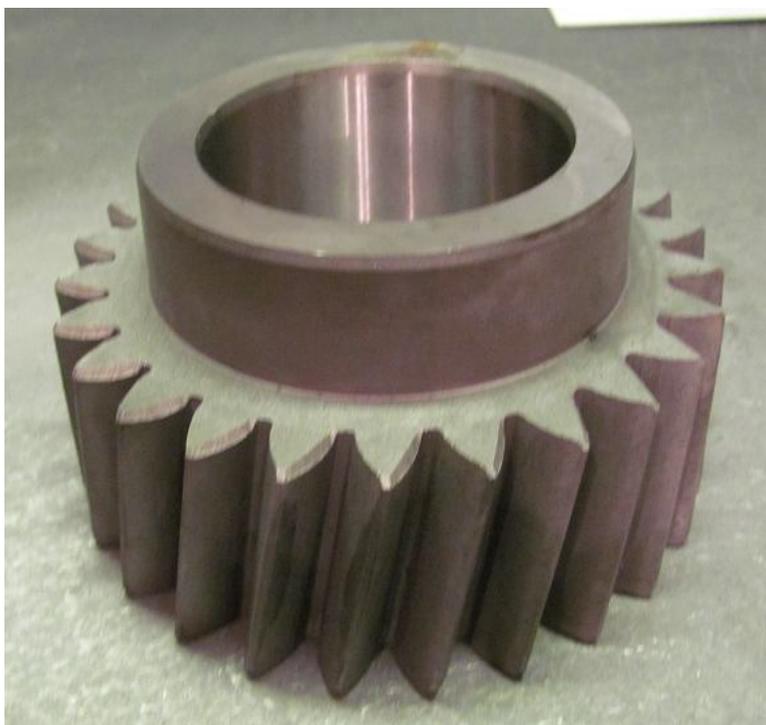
Шестерня 2-ой передачи промежуточного вала 1509.1701050
